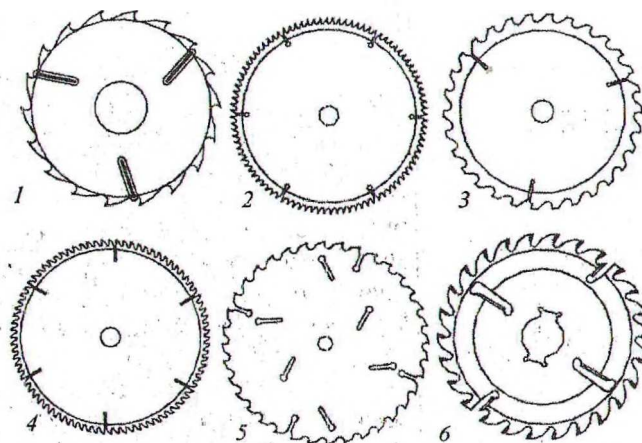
Конструкции пильных дисков с пластинками из твердого сплава
